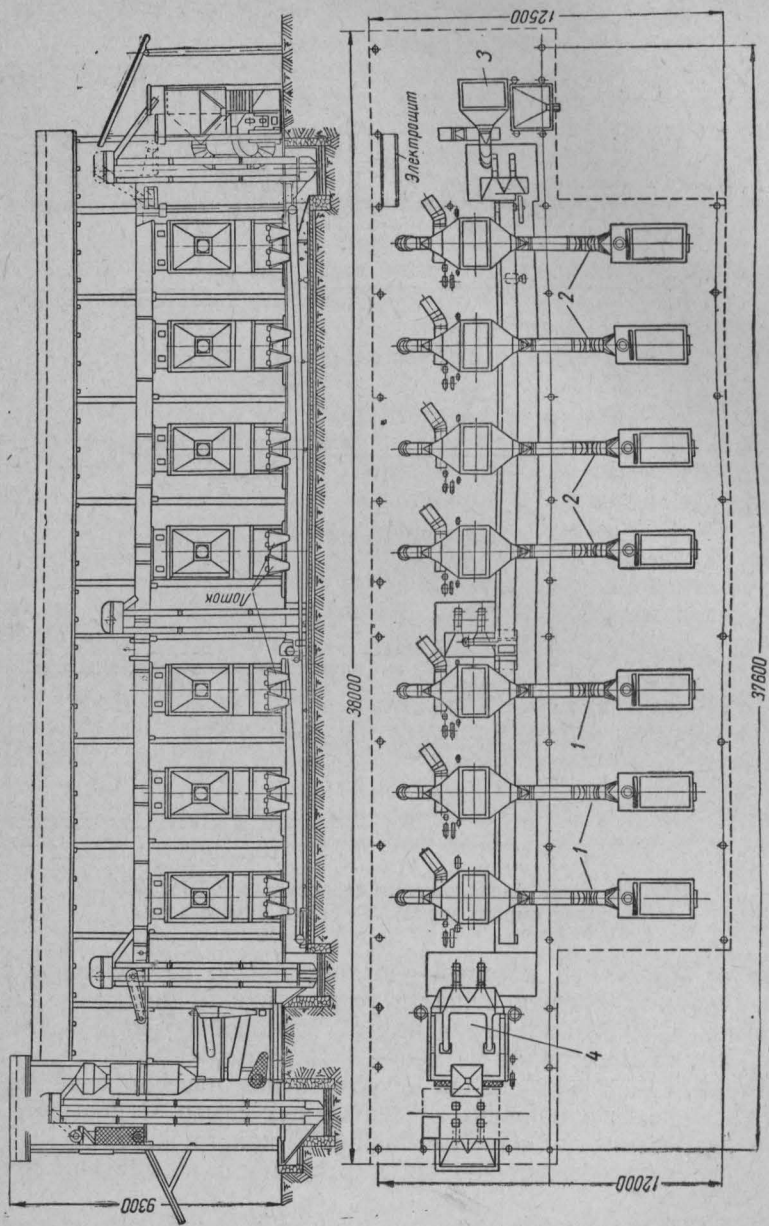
Восьмиагрегатная установка зерносушилок ВИСХОМ.
